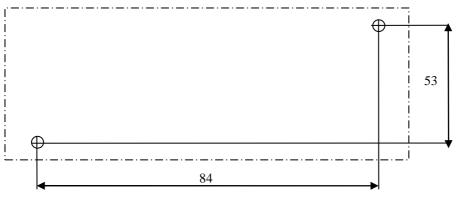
Разметка крепления корпуса УПВК-03П исп.2
